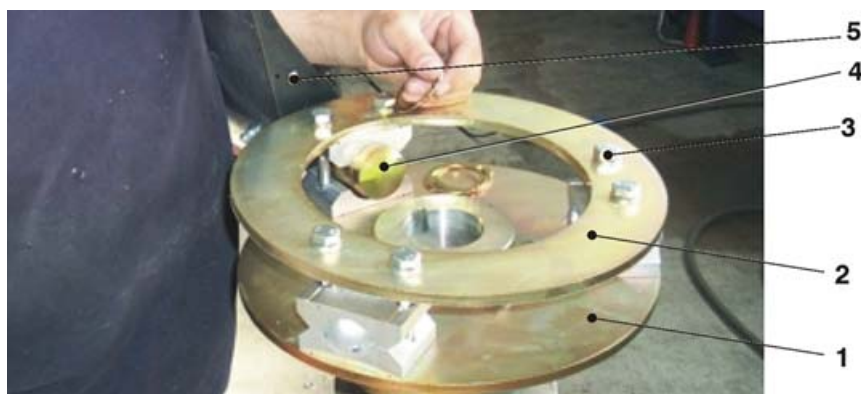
Montaggio delle pale disassemblate, preparazione disco.
